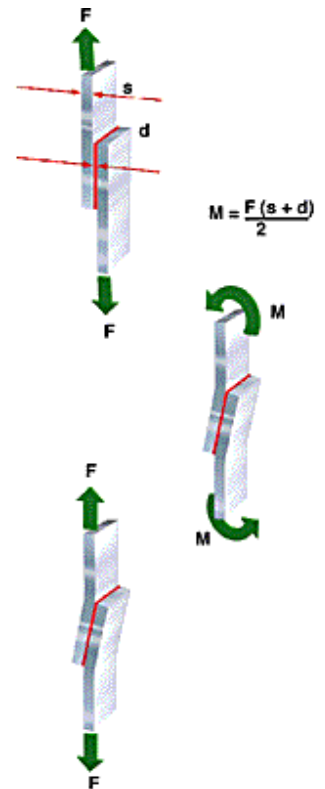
Deformación de una junta de solape simple causada por cargas excéntricas.
